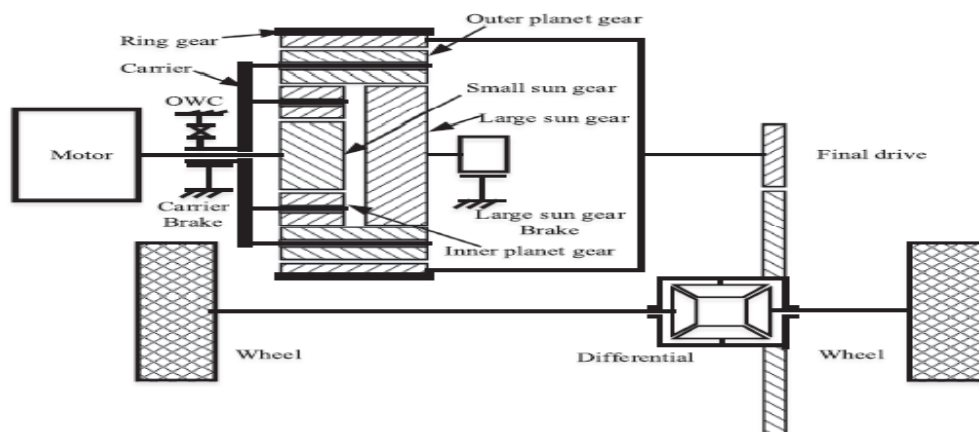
Partes de la Transmisión Epicycloidal
